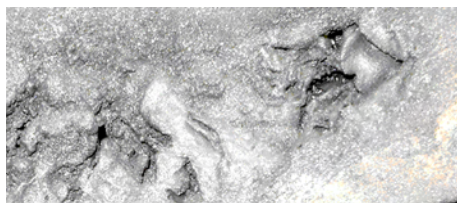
Дефект поверхности отливки "металлические плены"
